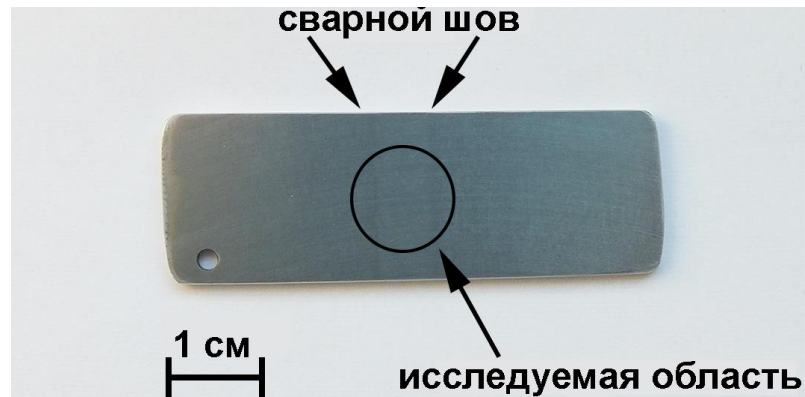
Фотография пластины из алюминиевого сплава 1579 со сварным швом, изготовленной для электрохимических испытаний. Исследуемая область отмечена окружностью
